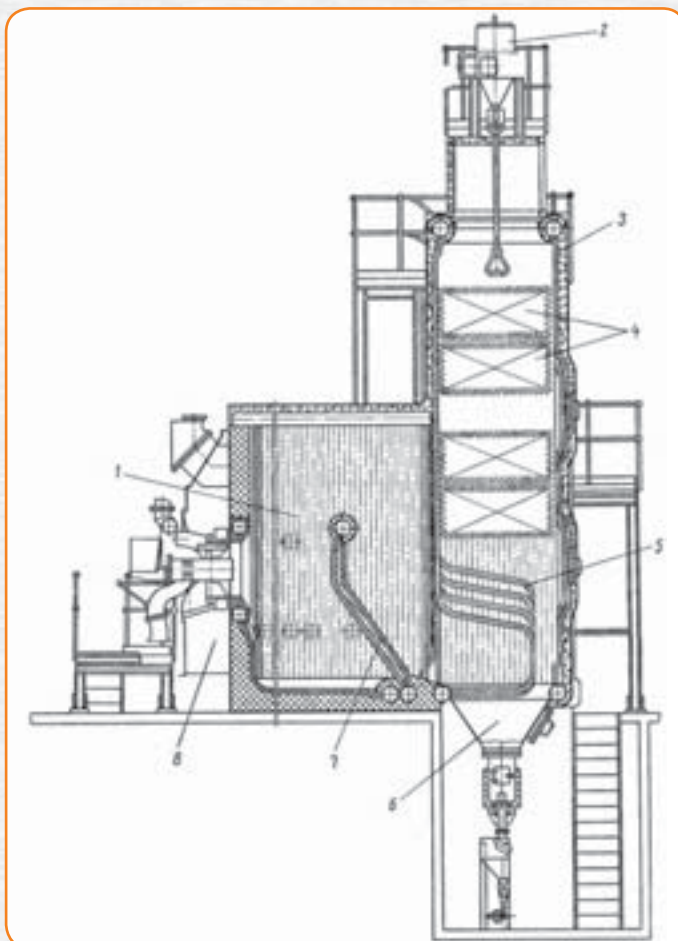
Водогрейный котел КВГМ: 1 – топочный блок; 2 – дробеструйная установка; 3 – конвективный блок; 4 – змеевики конвективных пакетов; 5 – фестон; 6 – бункер дробы; 7 – перегородка; 8 – горелочный короб
